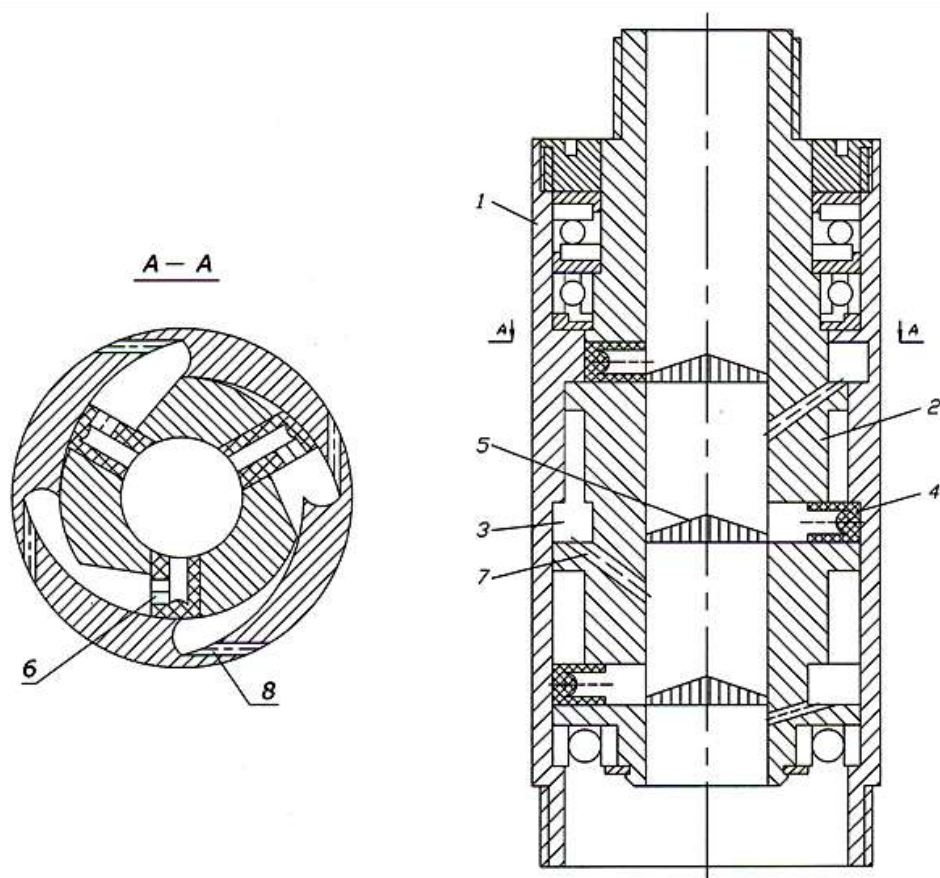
Забойный гидродвигатель ЗГД-70:
